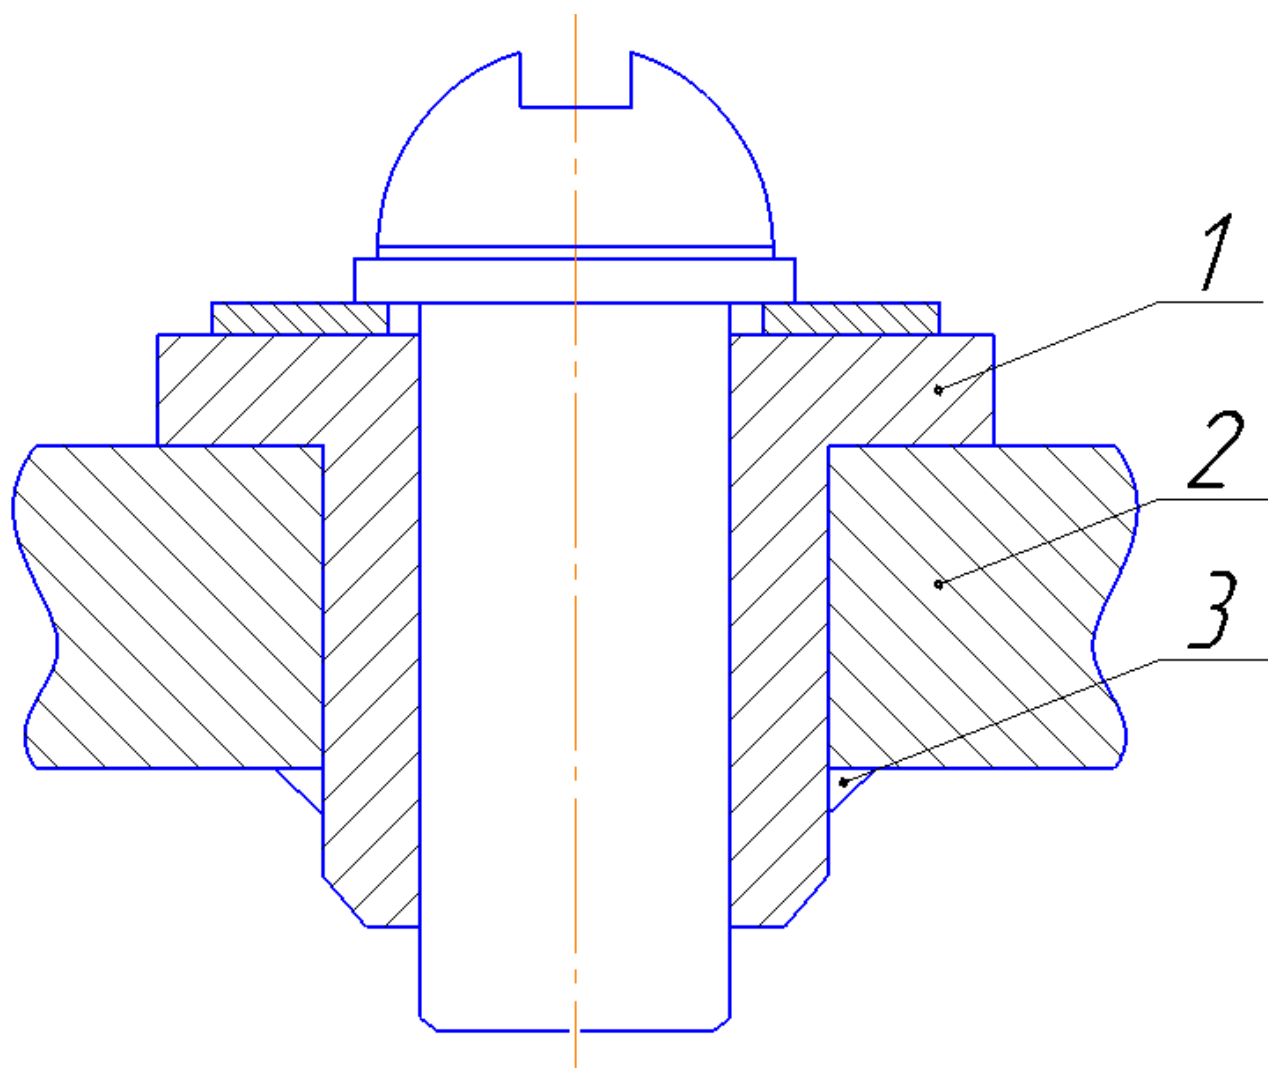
Увеличение длины резьбового отверстия привариванием втулки [2]:
